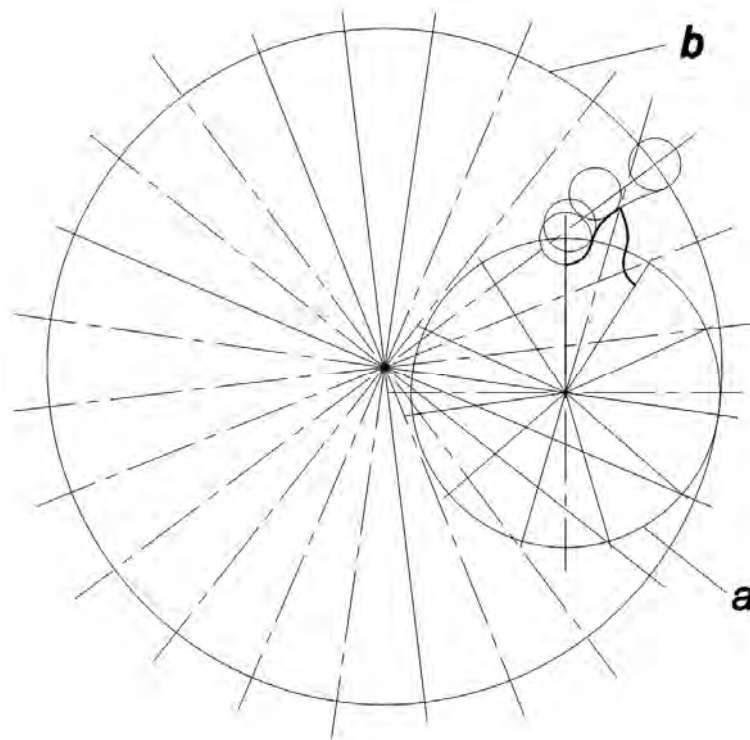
Сопряженный профиль зубьев сателлита при максимальном числе цевок центрального зубчатого колеса
